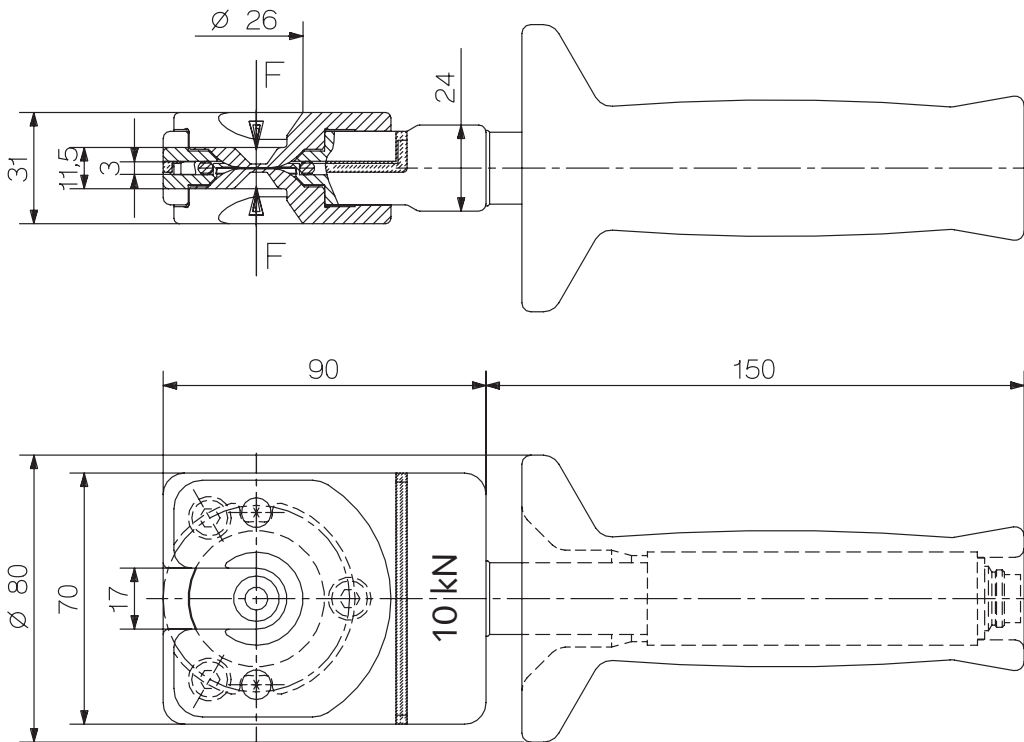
Schweisskraftsensor Typ 9831C... mit integriertem Ladungsverstärker und Kunststoffhandgriff (abnehmbar)
